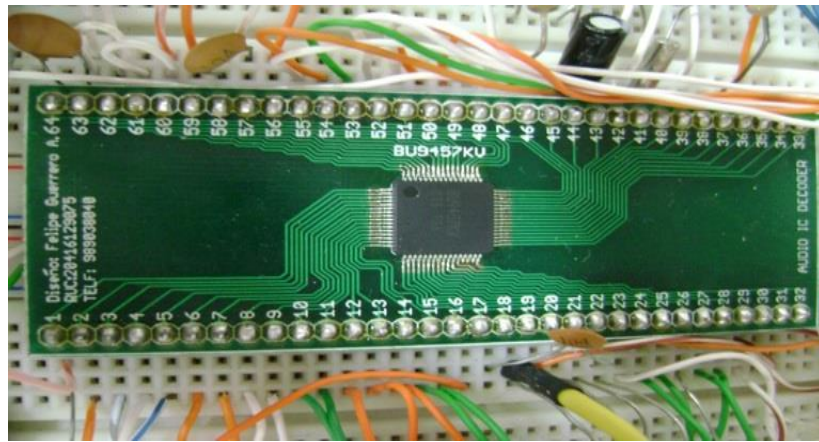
Módulo de pruebas BU9457KV para montaje sobre protoboard
